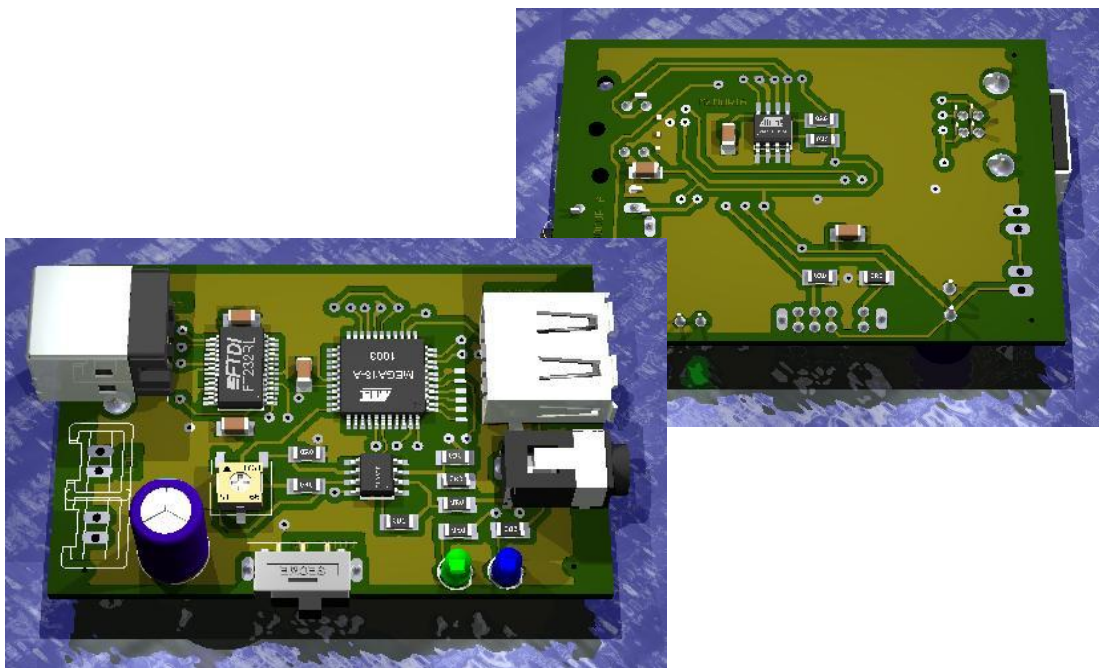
, PCB final del TR01 en 3D TOP y BOTTOM.
